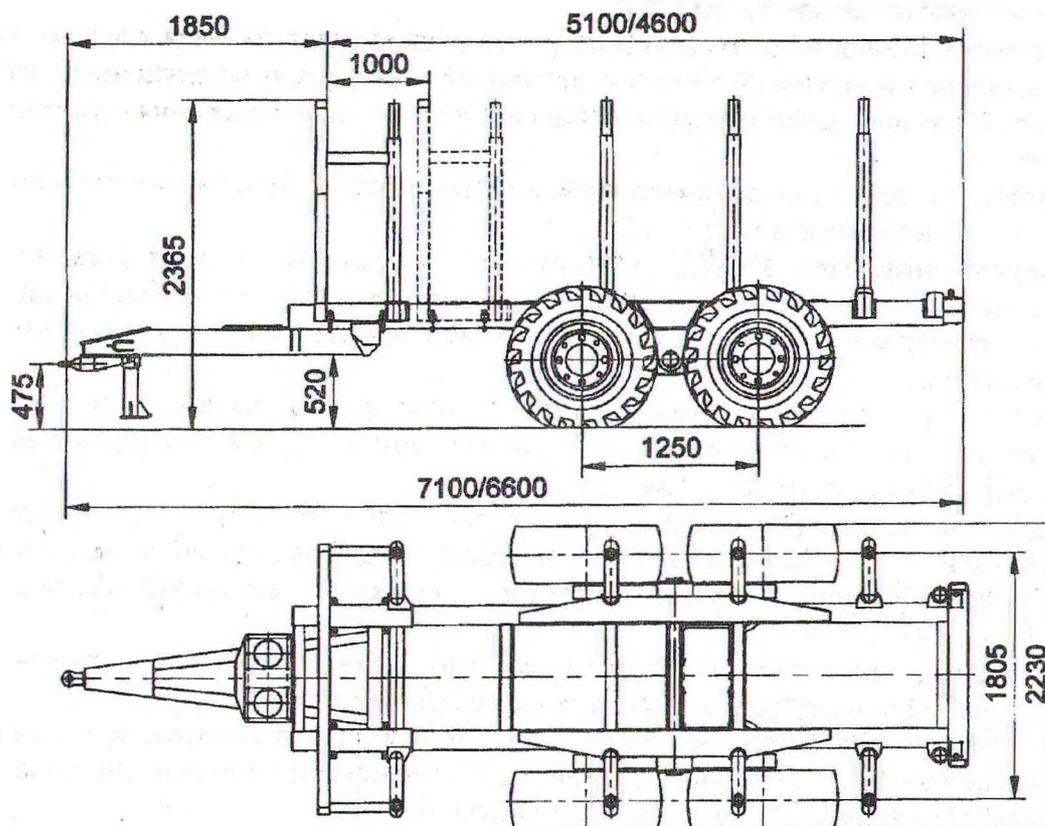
Габаритные размеры полуприцепа ПЛВ-9М/КМ
